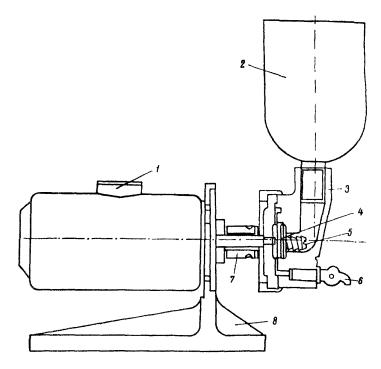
Схема диспергатора Союздорнии 1-электромотор УЛ-62 №-0,270 квт, 8000 об/мин ; 2-воронка; 3-корпус; 4-турбинка (смеситель); 5-шнек; 6-кран; 7-гайка; 8 - стойка
